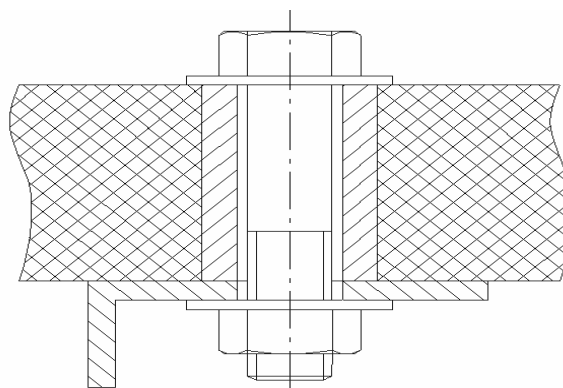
Конструкция подкрепления стенок отверстий в листовой заготовке из ПКМ
